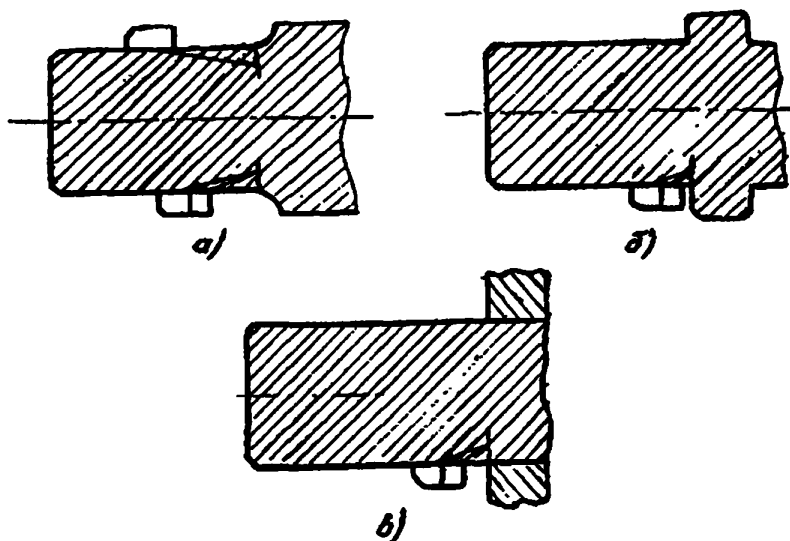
Примеры выявления трещин в валах поверхностными и головными волнами. - близких краев ступиц канатоведущих шкивов и внутренних колец подшипников (рис.21г);
